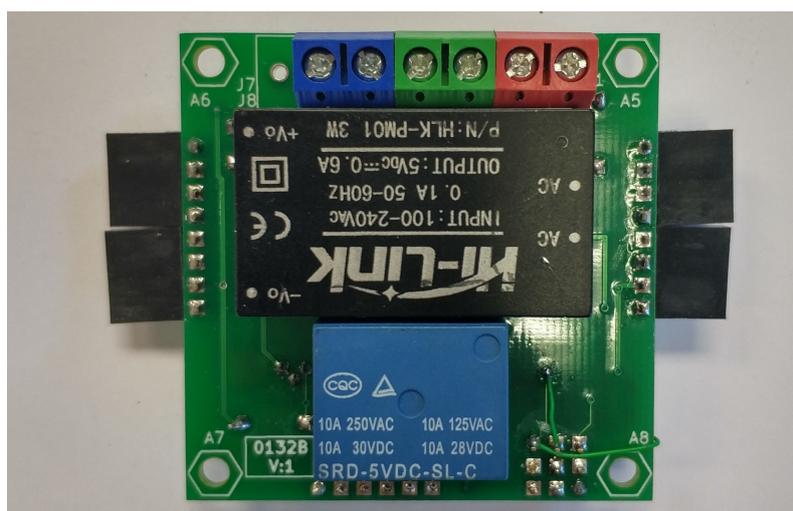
Montaje de la cara BOTTOM del Módulo de Alimentación.
